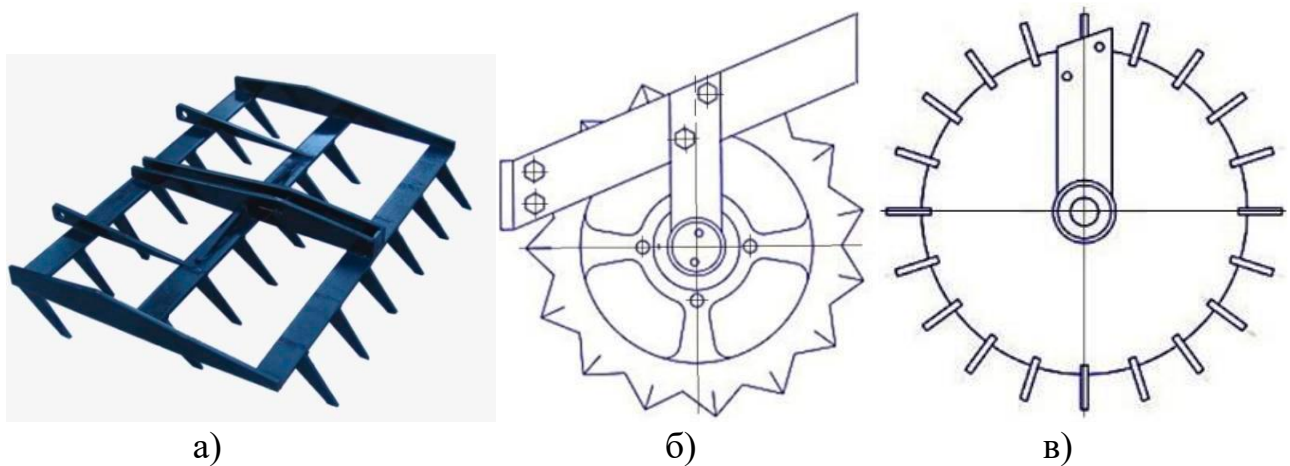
Додаткові робочі органи культиватора: а - борона; б - коток дисковий; в - коток рубчастий.
